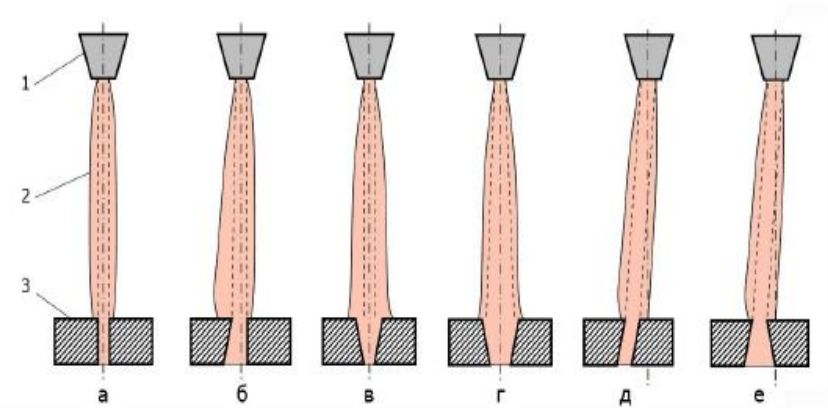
Признаки в следах газокислородной резки, позволяющие определить неисправность резака: а – нормальный рез; б – односторонний рез; в – оплавление верхних кромок металла; г – увеличение ширины реза; д – наклонный рез; е – расширение реза в нижней части (1 – горелка; 2 – режущая струя; 3 – разрезаемый металл)
